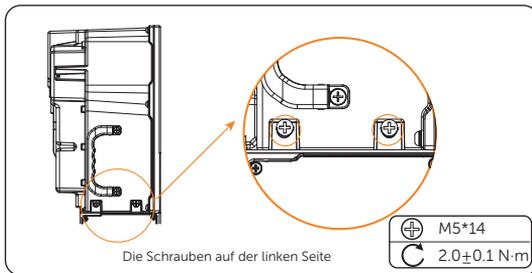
Die Schrauben auf der linken Seite sichern
